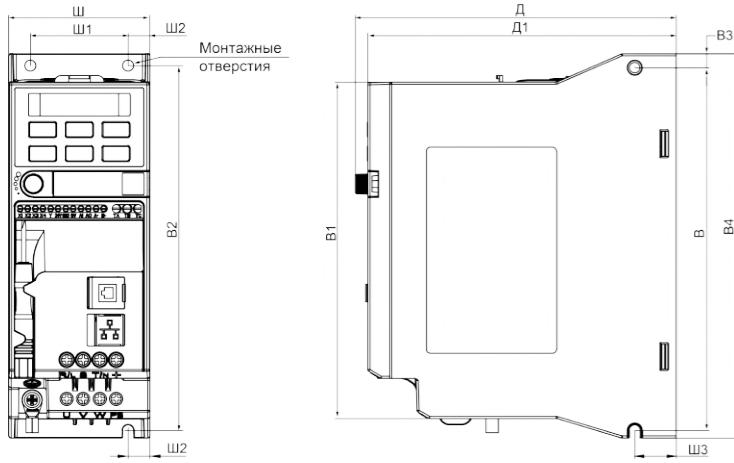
Габаритные и присоединительные размеры прибора типоразмеры 1 и 2
